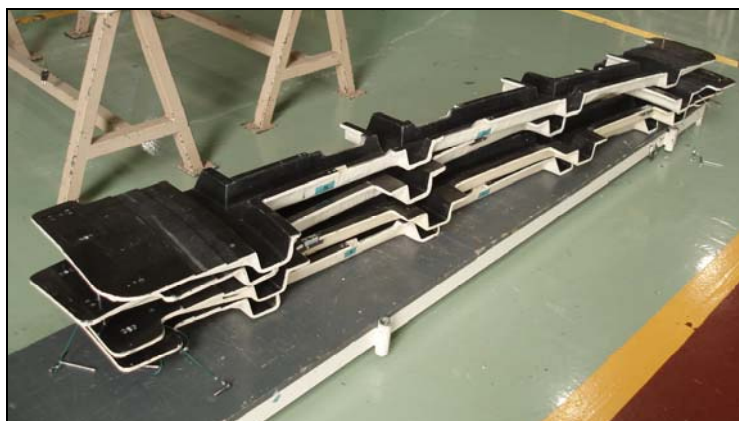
Carcasas para Posicionamiento de Vigas Transversales
